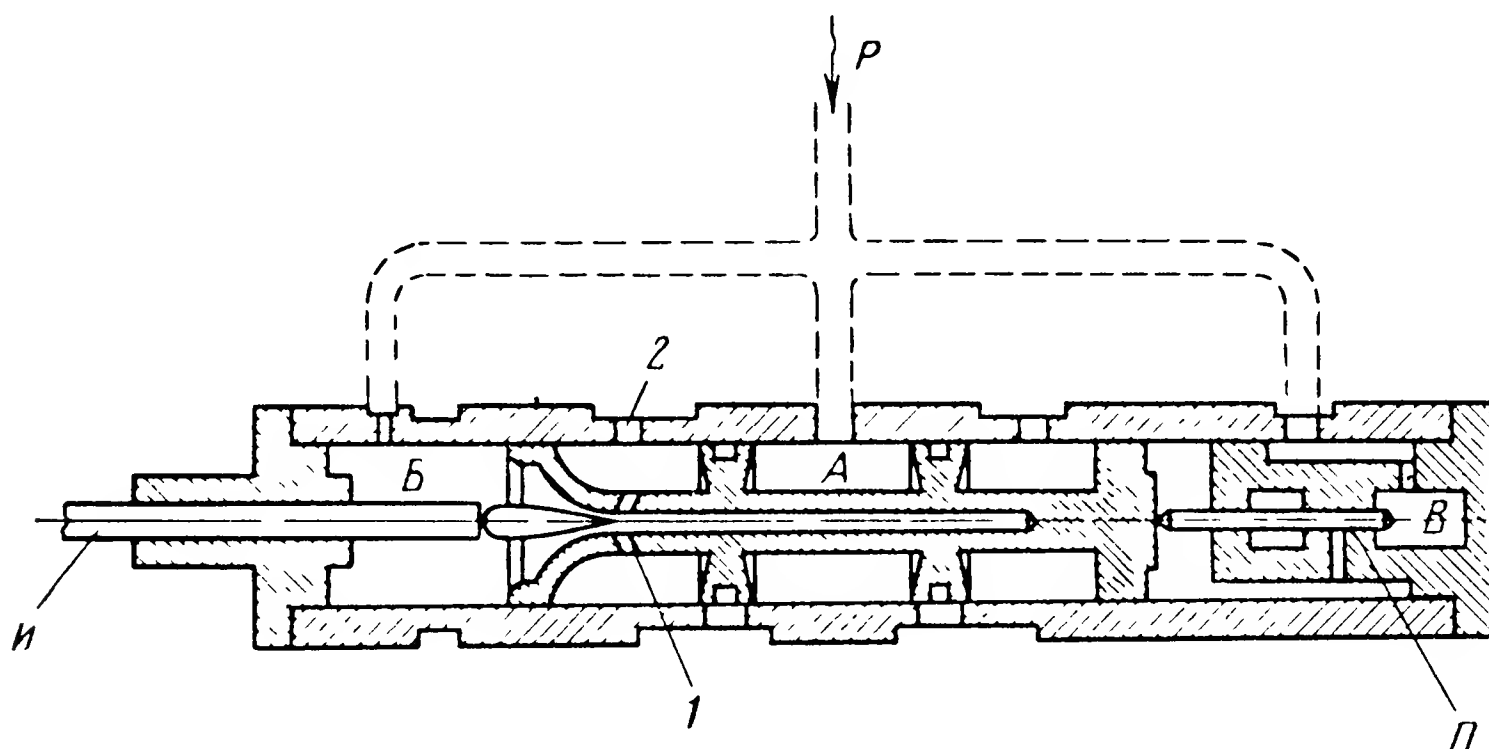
Конструкция золотника гидравлической рулевой машинки
